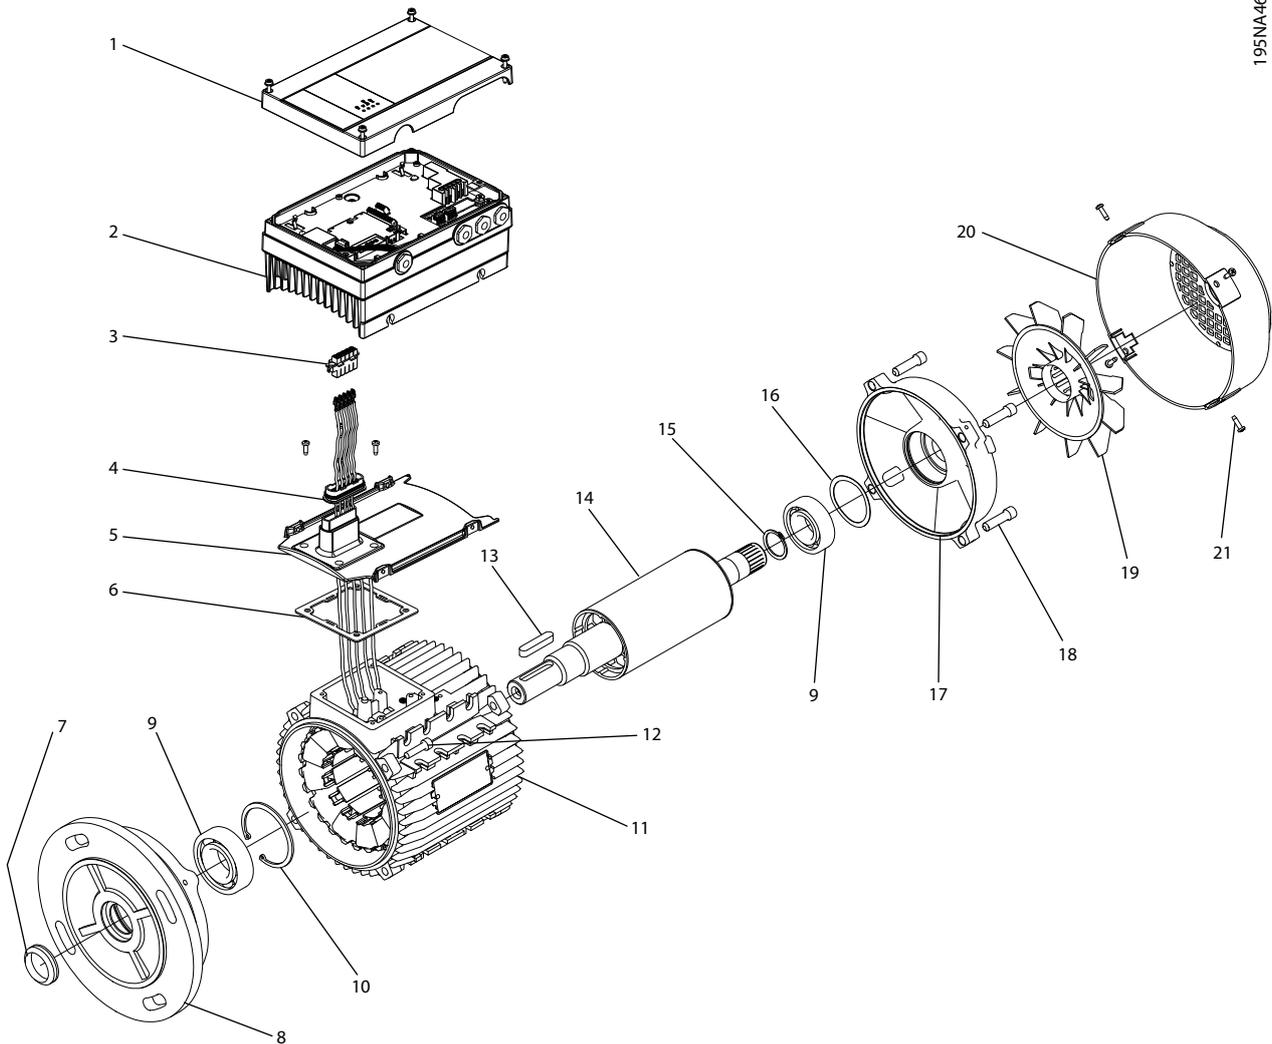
FCM 106 mit PM-Motor, Explosionszeichnung B5
